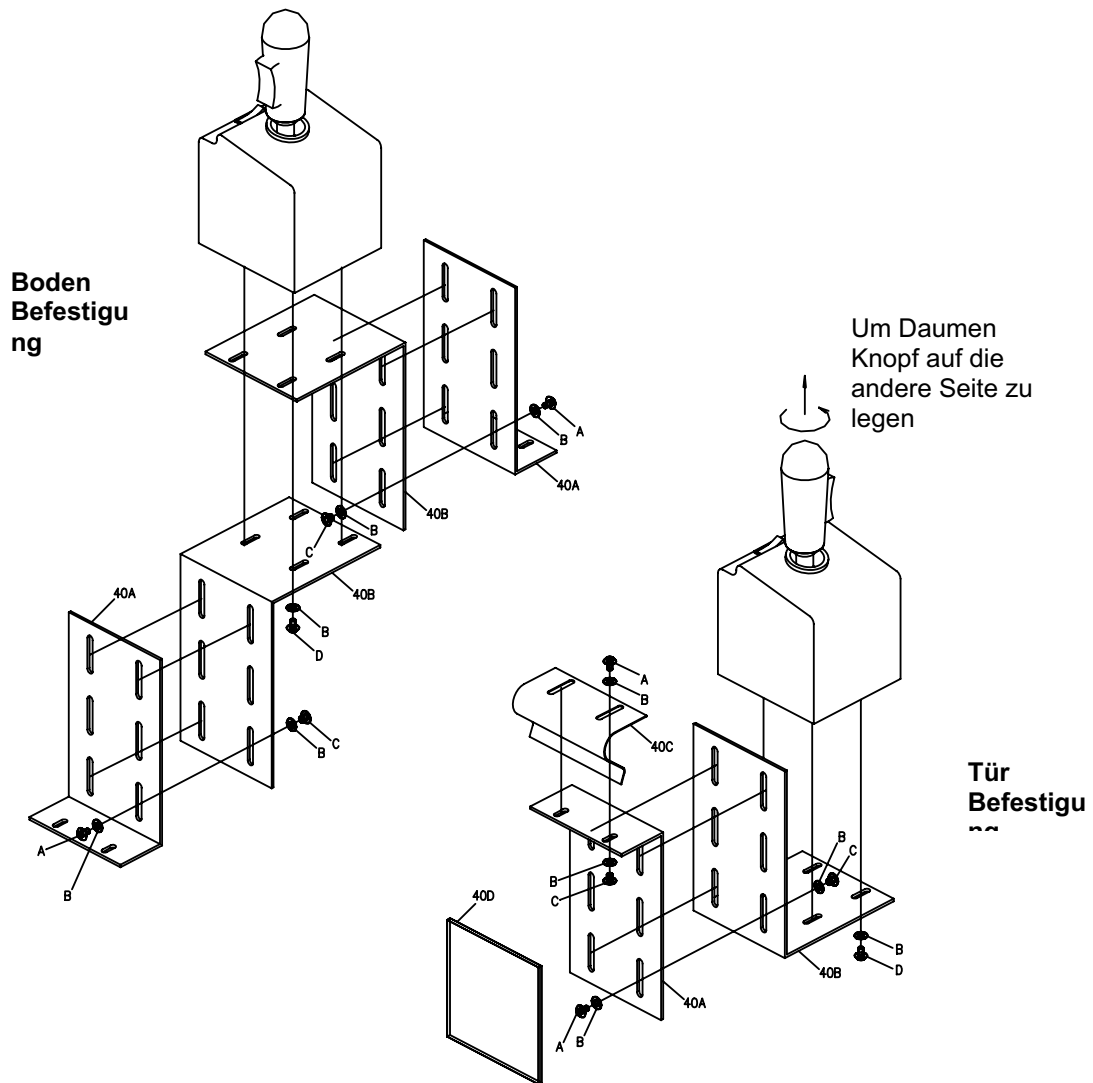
Joystick Steuerung Universal Befestigungs Kit Bauteile
